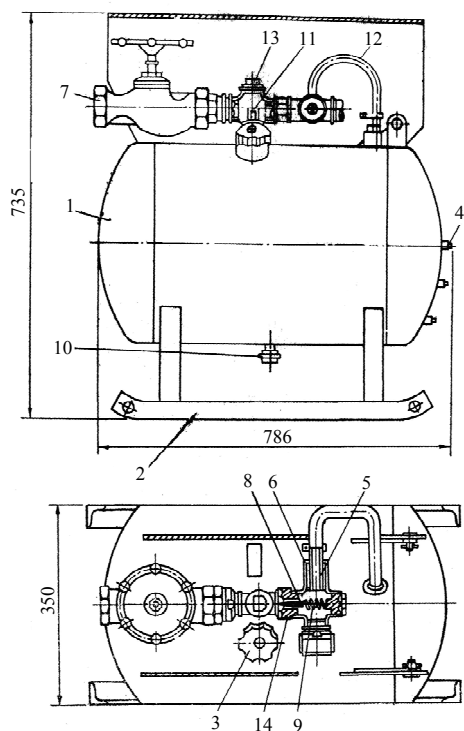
Дозатор смачивателя участкового ДСУ-4: 1 – резервуар; 2 – салазки; 3 – крышка резервуара; 4 – отверстие уровня; 5 – сменная насадка; 6 – гайка; 7 – вентиль; 8 – поплавок; 9 – пружина; 10 – пробка сливного отверстия; 11 – фильтр; 12 – трубка; 13 – кран; 14 – сопло
